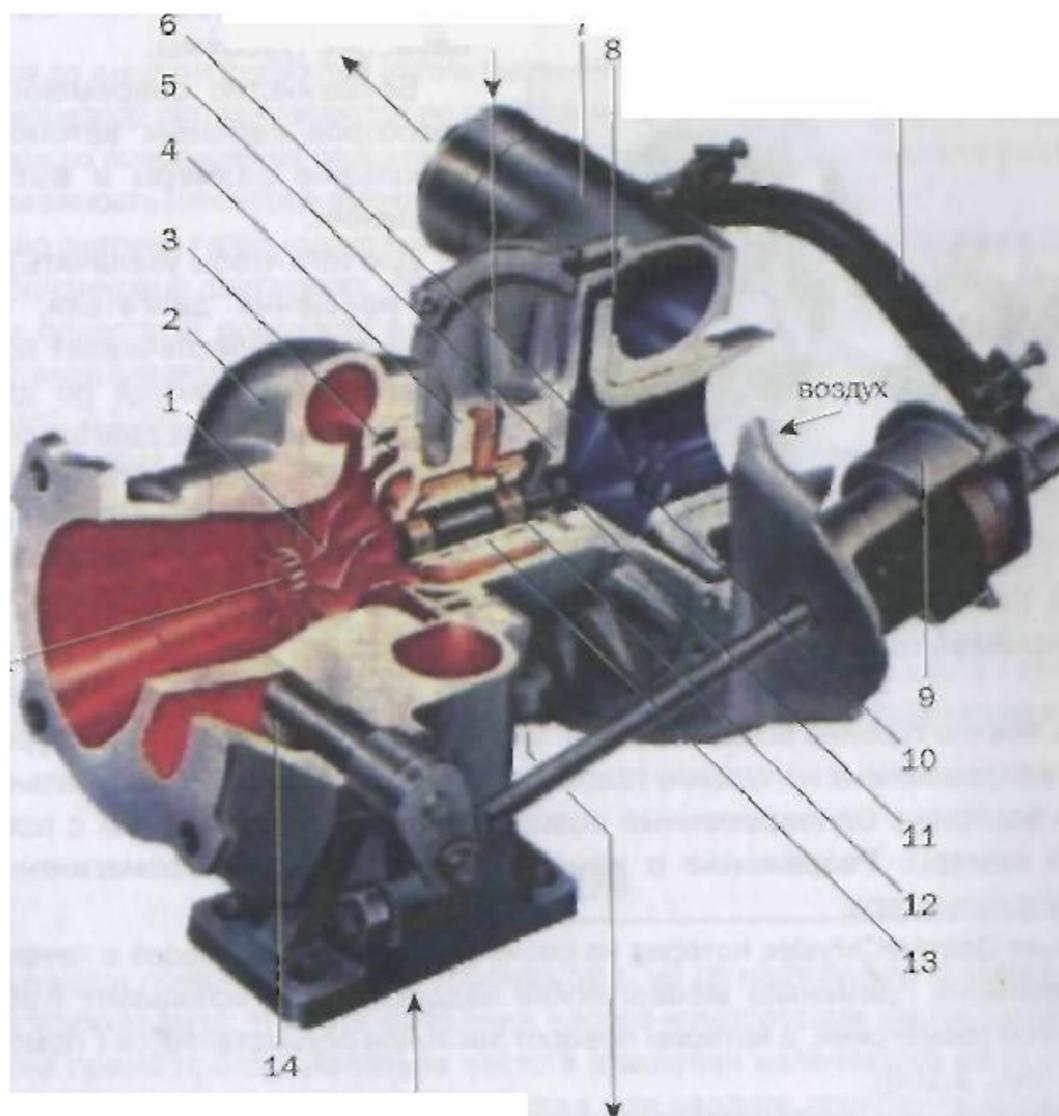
Турбокомпрессор Garrett: 1 - лопатки турбины; 2 - корпус турбины; 3 - тепловая защита; 4 - корпус подшипников; 5 - упор; 6 - защитная пластина; 7 - корпус компрессора; 8 - диффузор; 9 - клапан; 10 - насос компрессора; 11 - уплотнение; 12 - подшипник; 13 - втулка подшипника; 14 - заслонка
